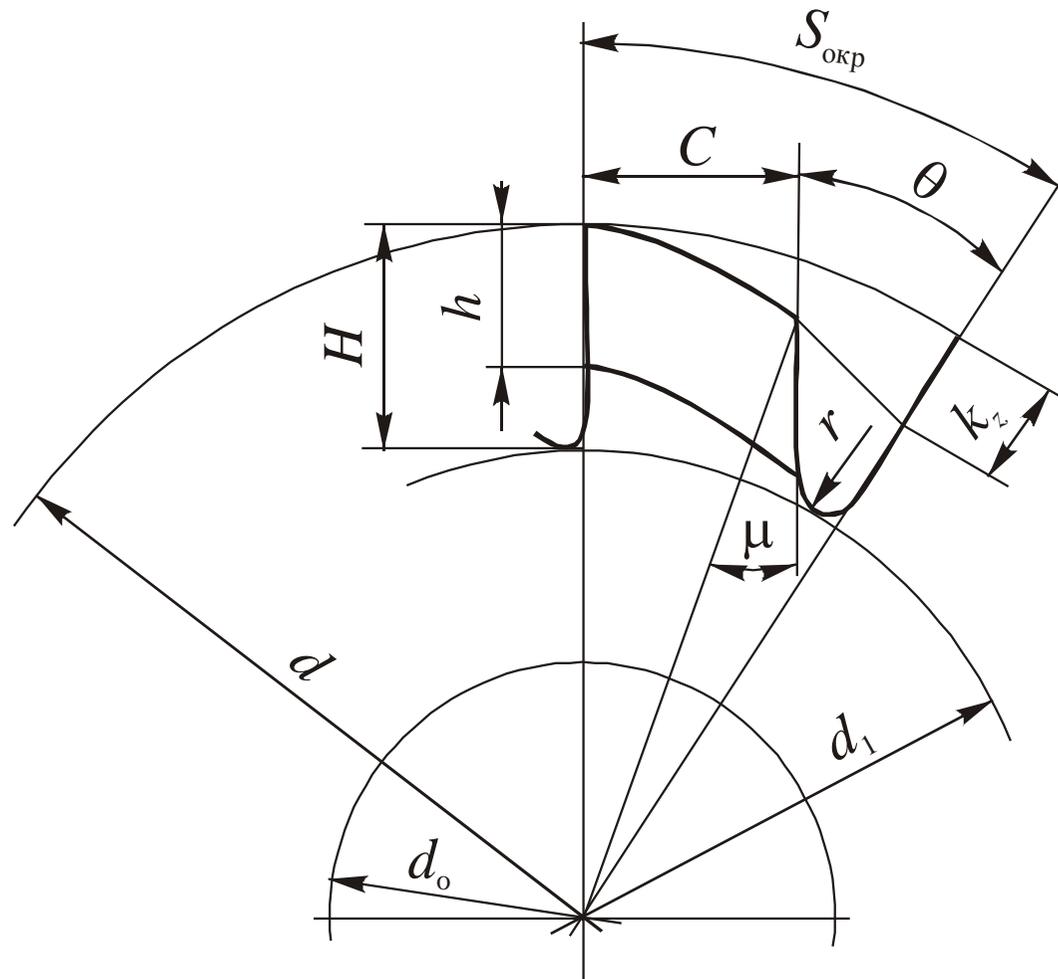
Конструктивные параметры фрезы с затылованными зубьями
